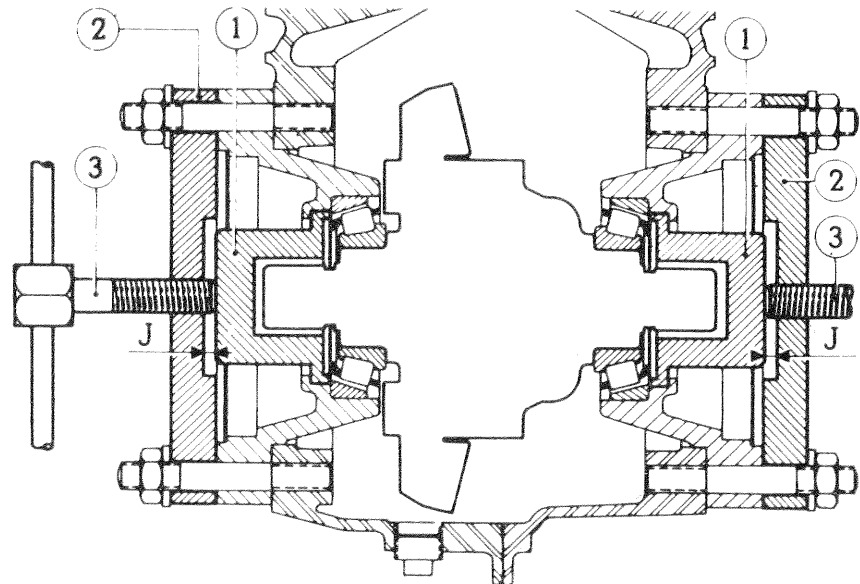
Mesure du jeu entre barreaux et poussoirs
